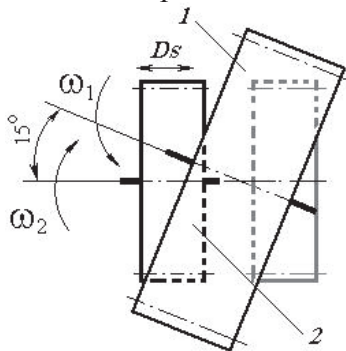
Схема основных движений при однопроходном шевинговании для стабилизации величины припуска под холодное накатывание зубьев:
